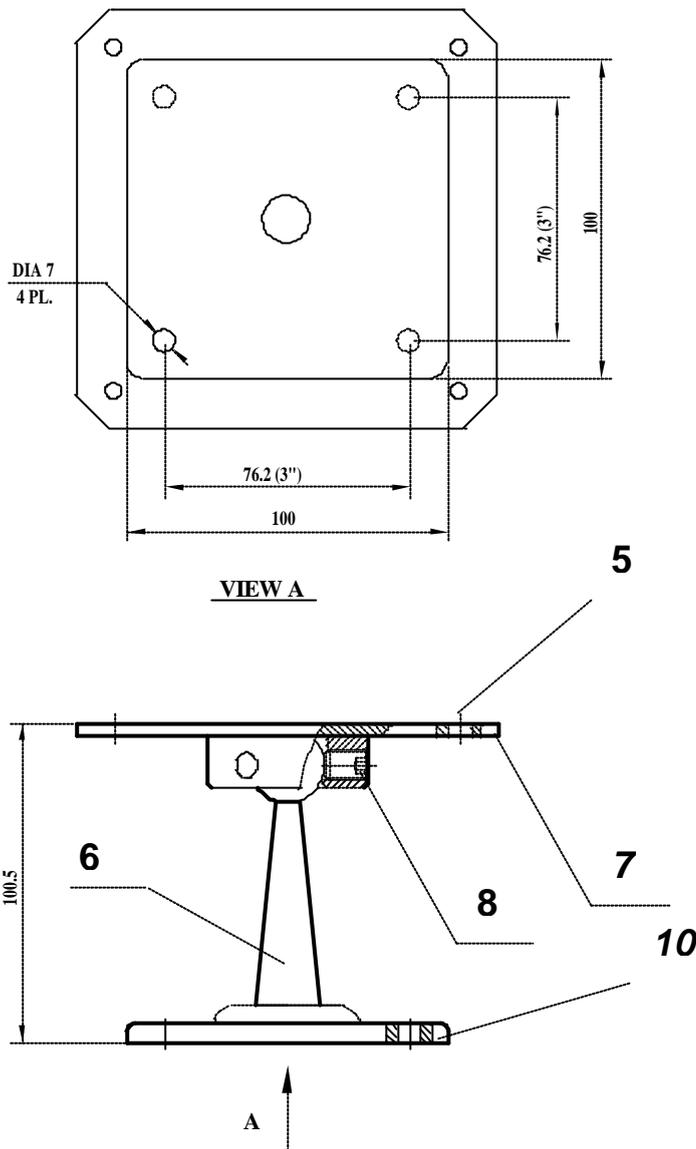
Montaje del soporte giratorio- Dibujo esquemático
